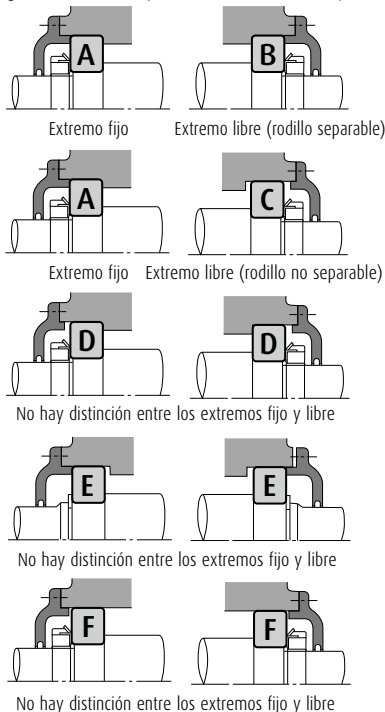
Disposición de montaje y tipos de rodamientos
